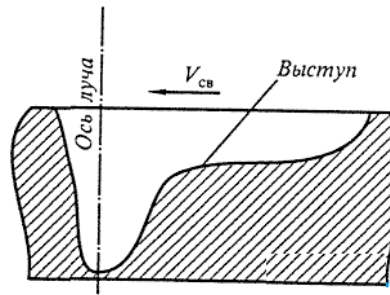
Продольное сечение сварочной ванны
